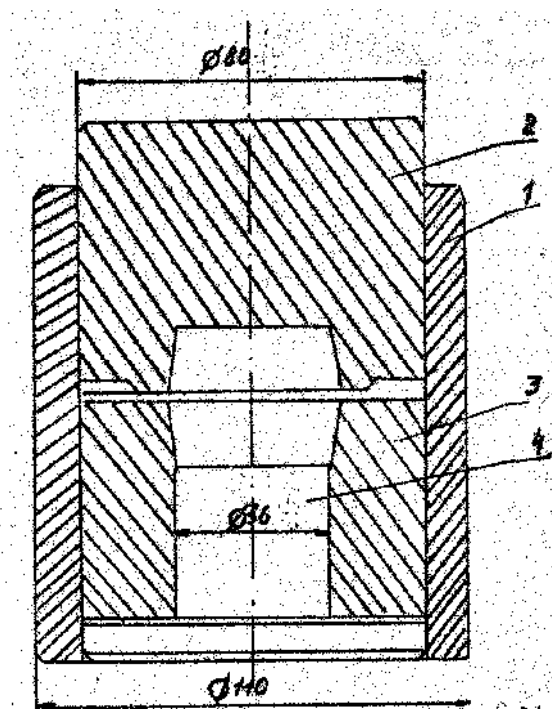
Штамп для открытой штамповки: 1 – направляющий стакан;
